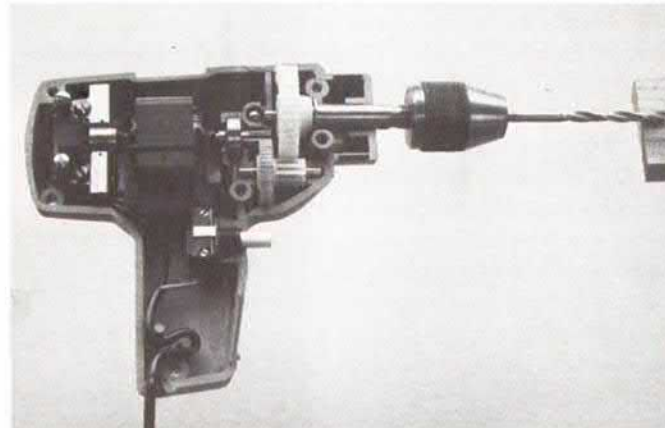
Elektrische Bohrmaschine für Kinder
